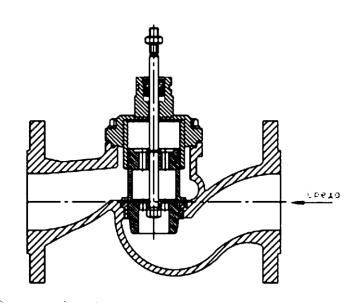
Клапан проходной односедельный запорно-регулирующий КПСР
